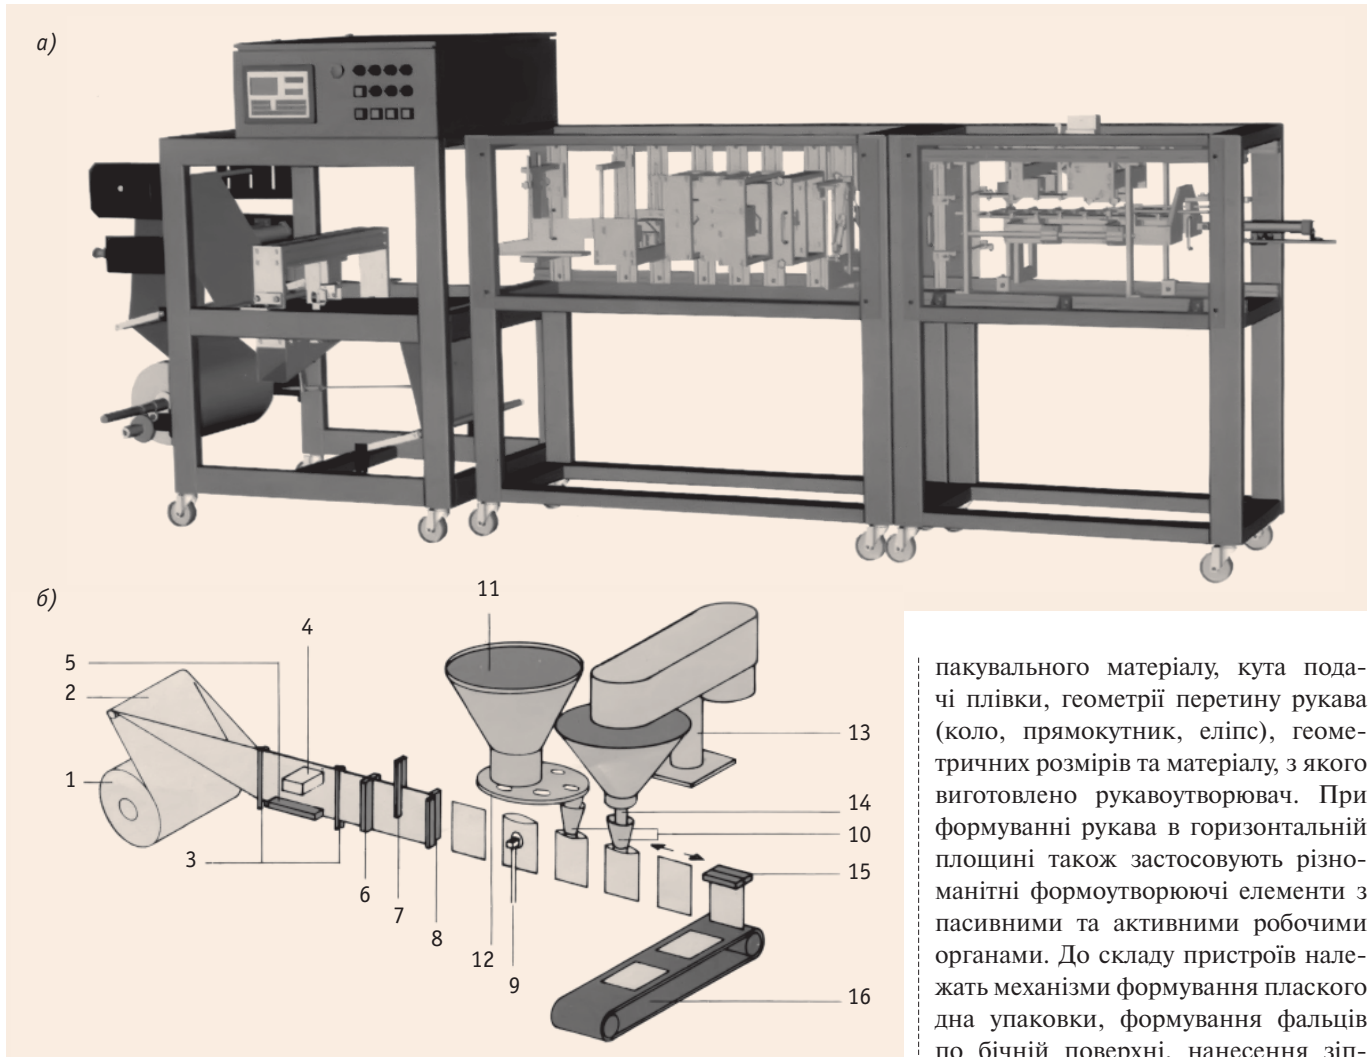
Формування упаковки із чотирма швами з рулонного термоварного матеріалу горизонтальним способом: а – загальний вигляд машини; б – технологічна схема: 1 – рулон матеріалу; 2 – пристрій плоского складання пакувального матеріалу; 3 – напрямні для плівки; 4 – фотодатчик; 5 – пристрій нижнього поздовжнього зварювання; 6 – пристрій поперечного зварювання; 7 – захоплювальний пристрій; 8 – пристрій відрізання; 9 – вакуумний захоплювач; 10 – насадки; 11 – бункер дозатора; 12 – ротор дозатора; 13 – рама дозатора; 14 – шнековий дозатор; 15 – пристрій верхнього поздовжнього зварювання; 16 – конвеєр відведення продукції
